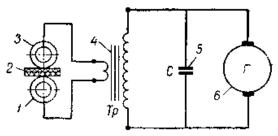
Схема сварки пластмасс токами высокой частоты:
